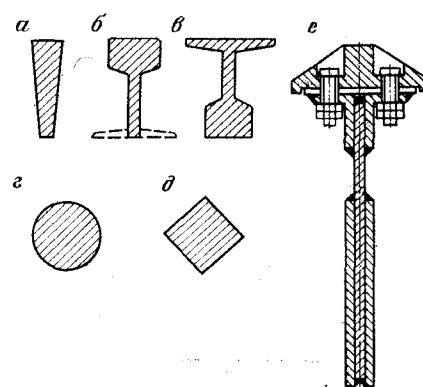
Сечение колосников. а — трапециевидное; б — рельс со срезанной подошвой; в — рельс подошвой вверх; г — круглое; д — квадратное; е — сварная балка с броней из марганцовистой стали
